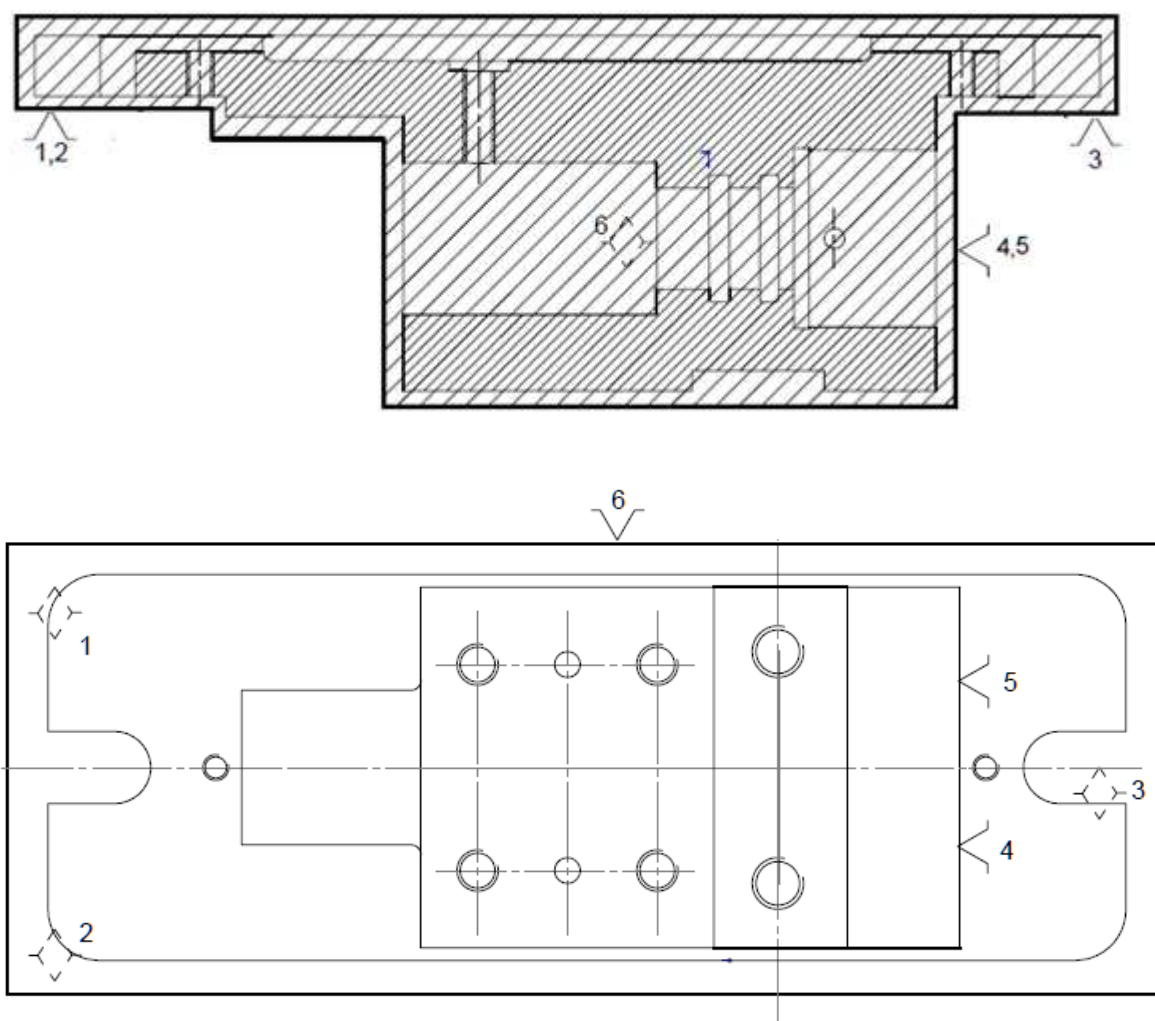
Теоретична схема базування по технологічним базам деталі «Корпус»
